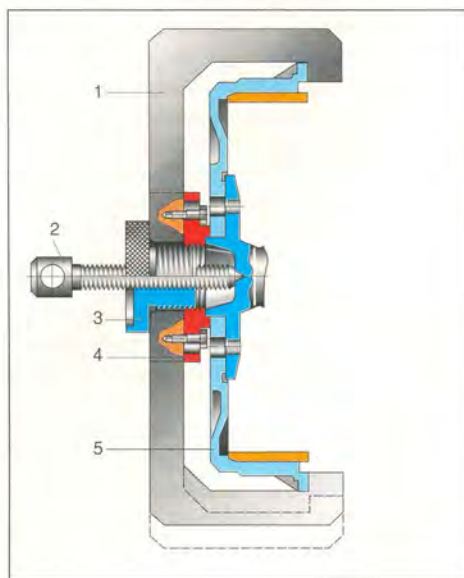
Съемник тормозного барабана: 1 – захват (3 шт.); 2 – болт; 3 – резьбовая втулка; 4 – ступица; 5 – барабан.
